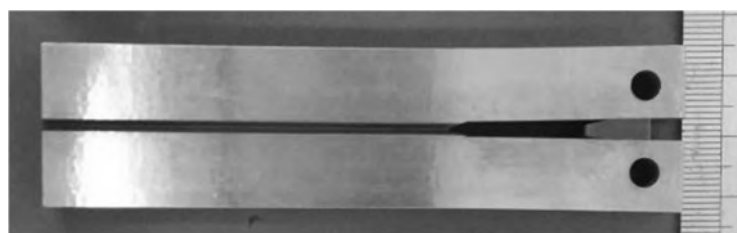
Corpo de prova DCB com a cunha posicionada para produzir o deslocamento constante.
